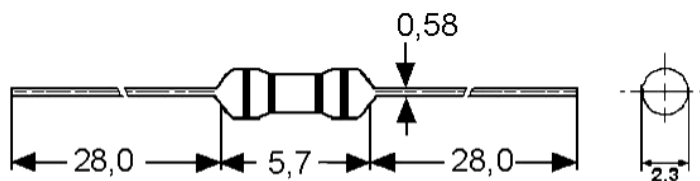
Габаритні розміри резистора типу MF-25
